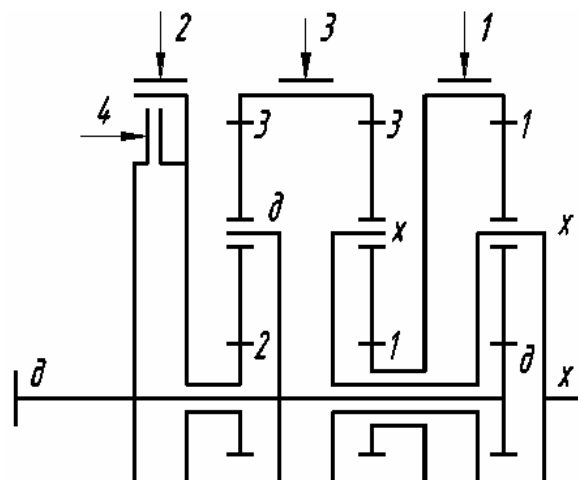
Кинематическая схема коробки передач № 1, 6, 8
